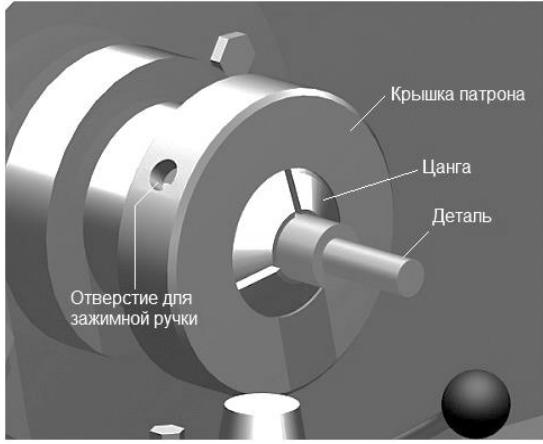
Патрон с цангой для закрепления заготовок с круглым поперечным сечением по наружной поверхности
